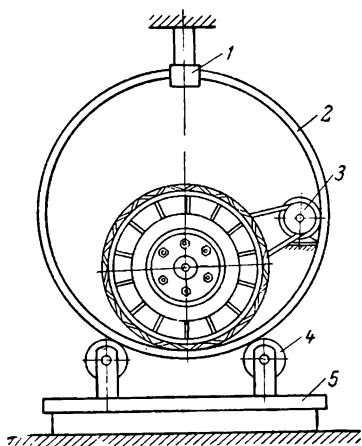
Станок для обкатки шины по внутренней поверхности кольцеобразного барабана:
